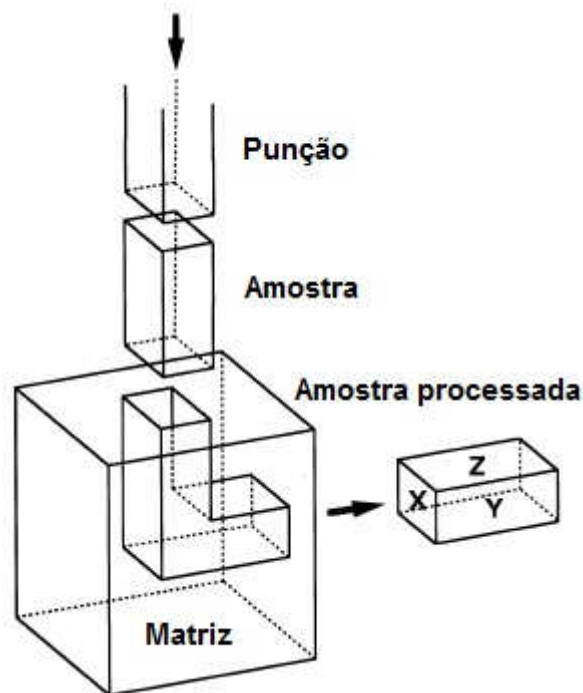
Ilustração esquemática de uma matriz de ECAP típica: os planos X, Y e Z denotam o plano transversal, o plano de fluxo e o plano longitudinal, respectivamente.
